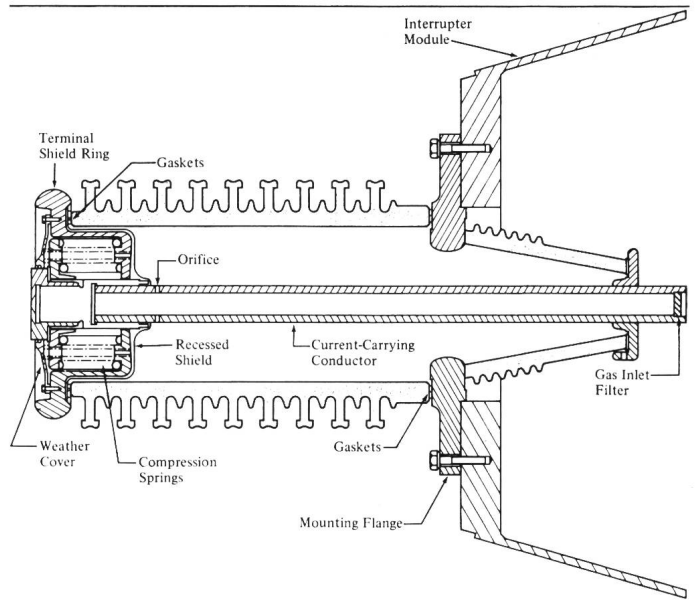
Porzellan durchführung mit SF_6 -Füllung
